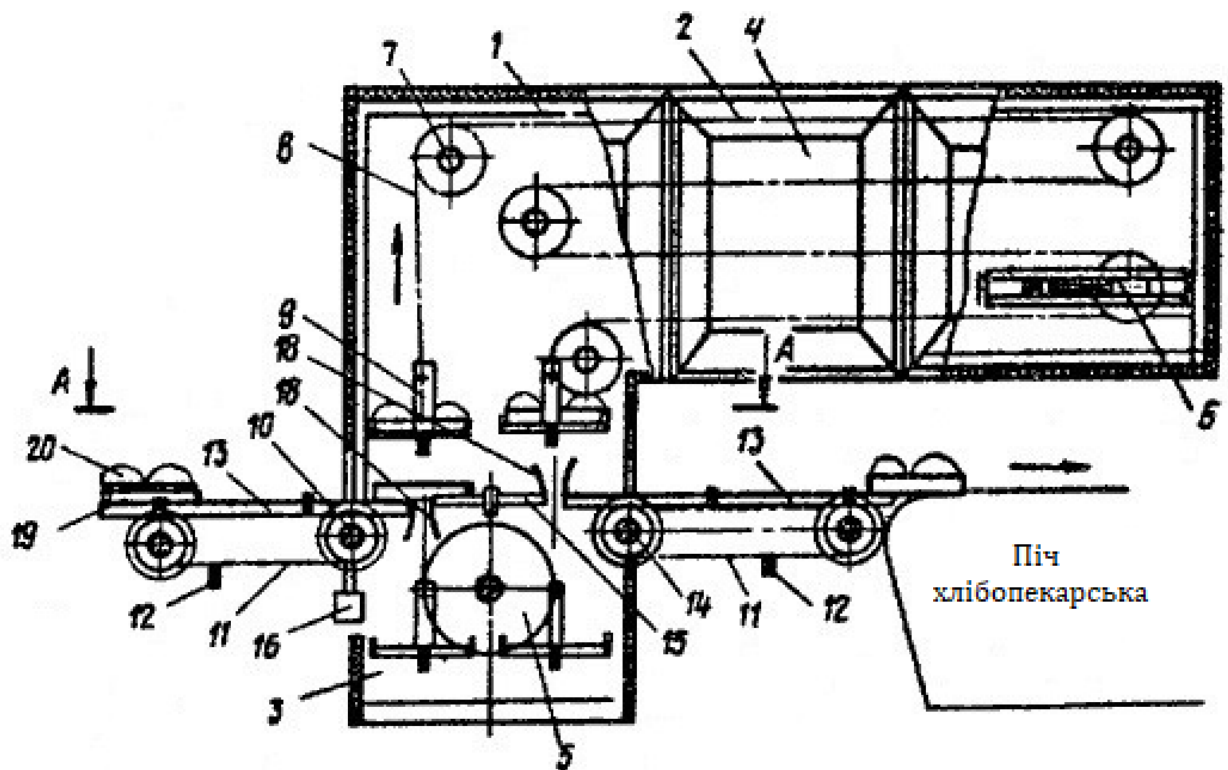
Пристрій для вистоювання тістових заготовок
